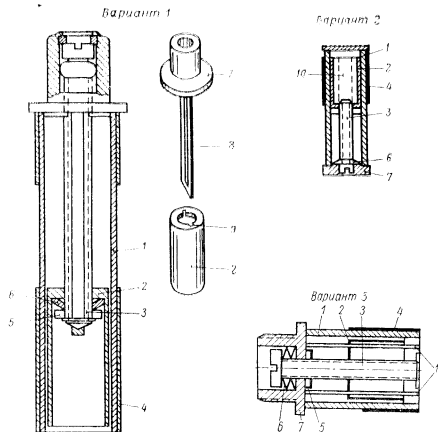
Поршневой цилиндрический конденсатор с поступательным движением поршня
